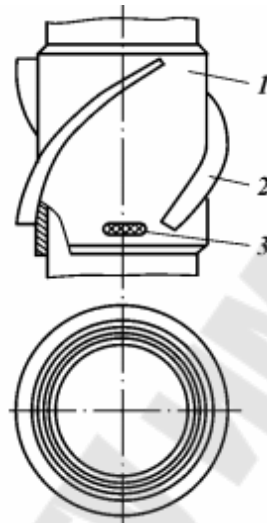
Турбулизатор типа ЦТ: 1- корпус неразъемный; 2-лопасть;3- клин спиральный
